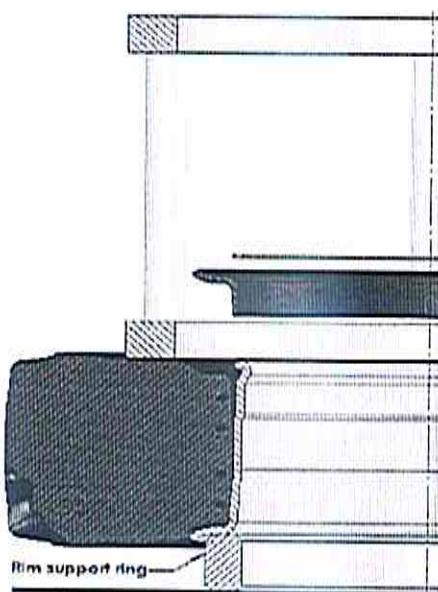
Схема установки большого (одинарного) запорного кольца
